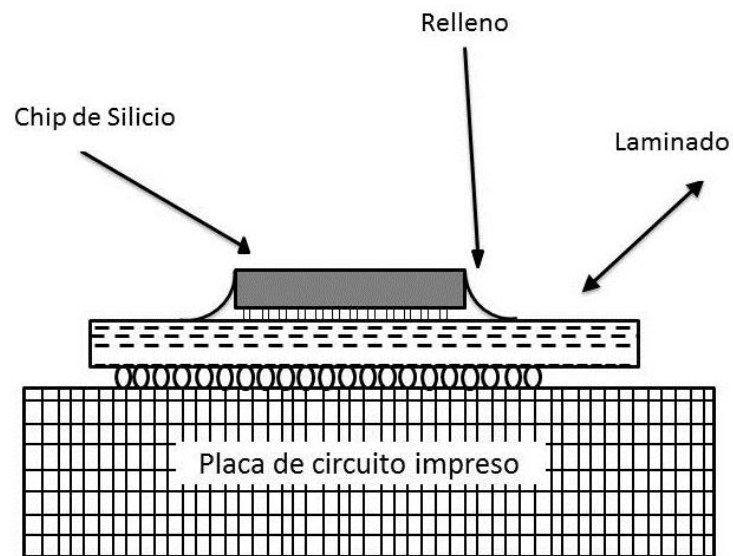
Flip Chip ensamblado sobre un BGA [2].
